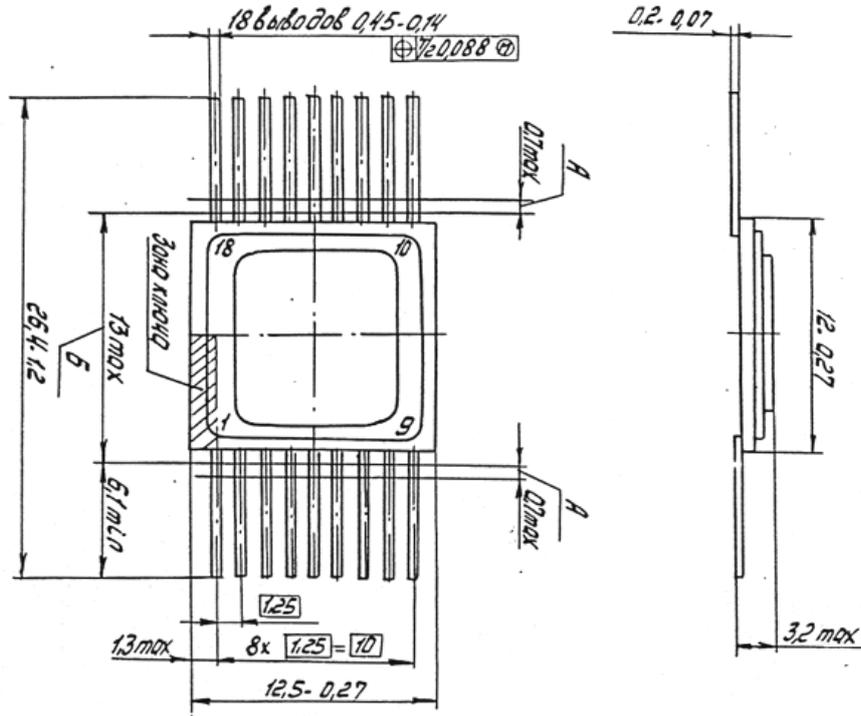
Габаритный чертеж корпуса 427.18-2.03
